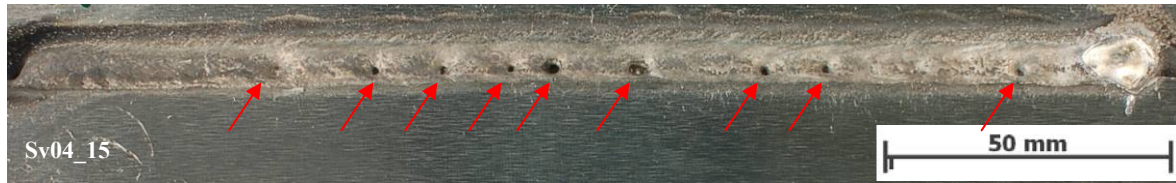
Nicht ausfließendes Schweißgut AlMg5 bei zu geringer Wärmeeinbringung in das Schweißblech beim verschweißen von AW-5083-O
